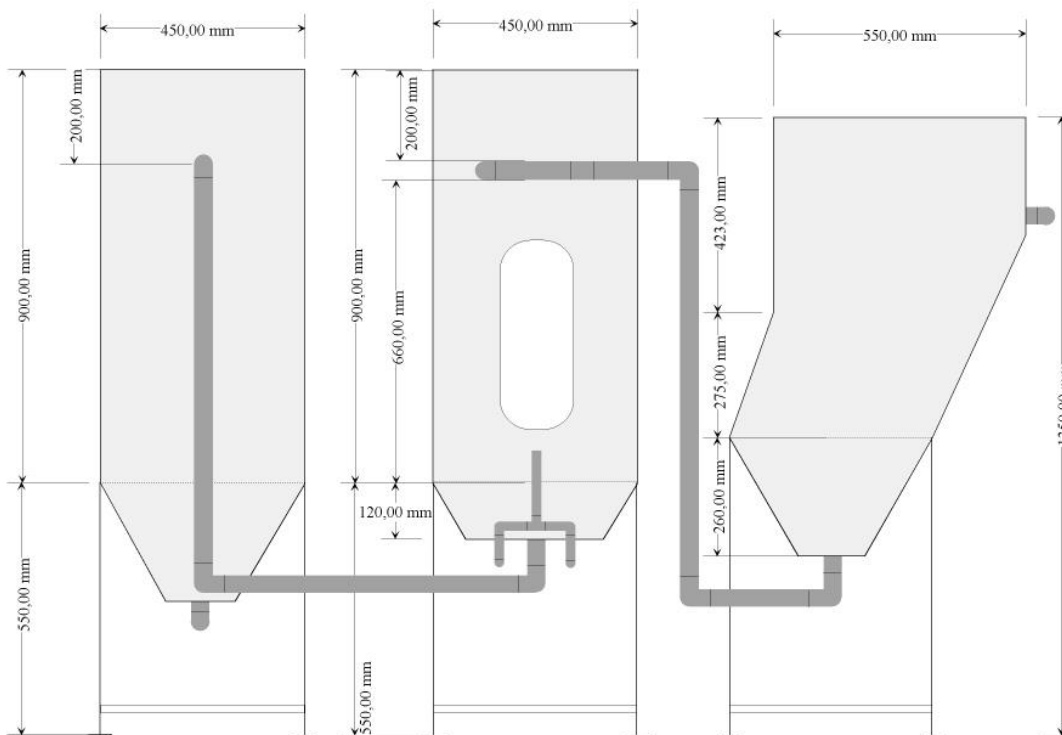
Esquema en alzado de los componentes principales de la planta piloto.
